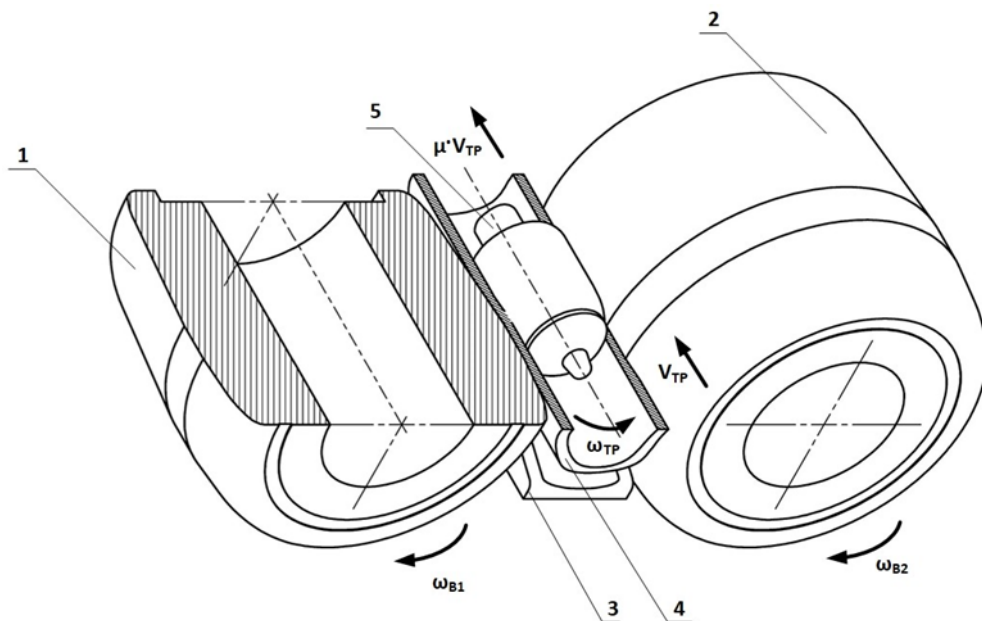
Схема процесса обкатки: 1, 2 – валки обкатного стана; 3 – направляющая проводка; 4 – труба; 5 – оправка
